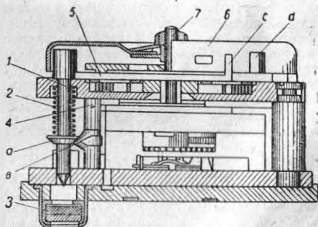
Часовой и дистанционный механизмы трубки Круппа:
